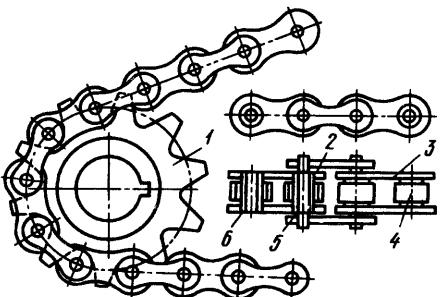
Цепная передача с втулочно-роликовой цепью
